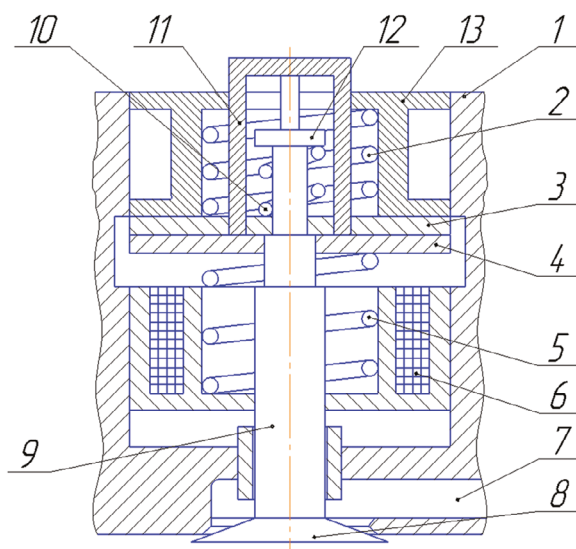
Электромагнитная система управления клапанами механизма газораспределения ДВС: 1 — корпус; 2 — пружина; 3 — металлическая пластина; 4 — дисковый якорь; 5 — пружина; 6 — обмотка нижнего электромагнита; 7 — газовый канал; 8 — тарелка клапана; 9 — ножка клапана; 10 — пружина; 11 — взводная вилка; 12 — упор; 13 — корпус
